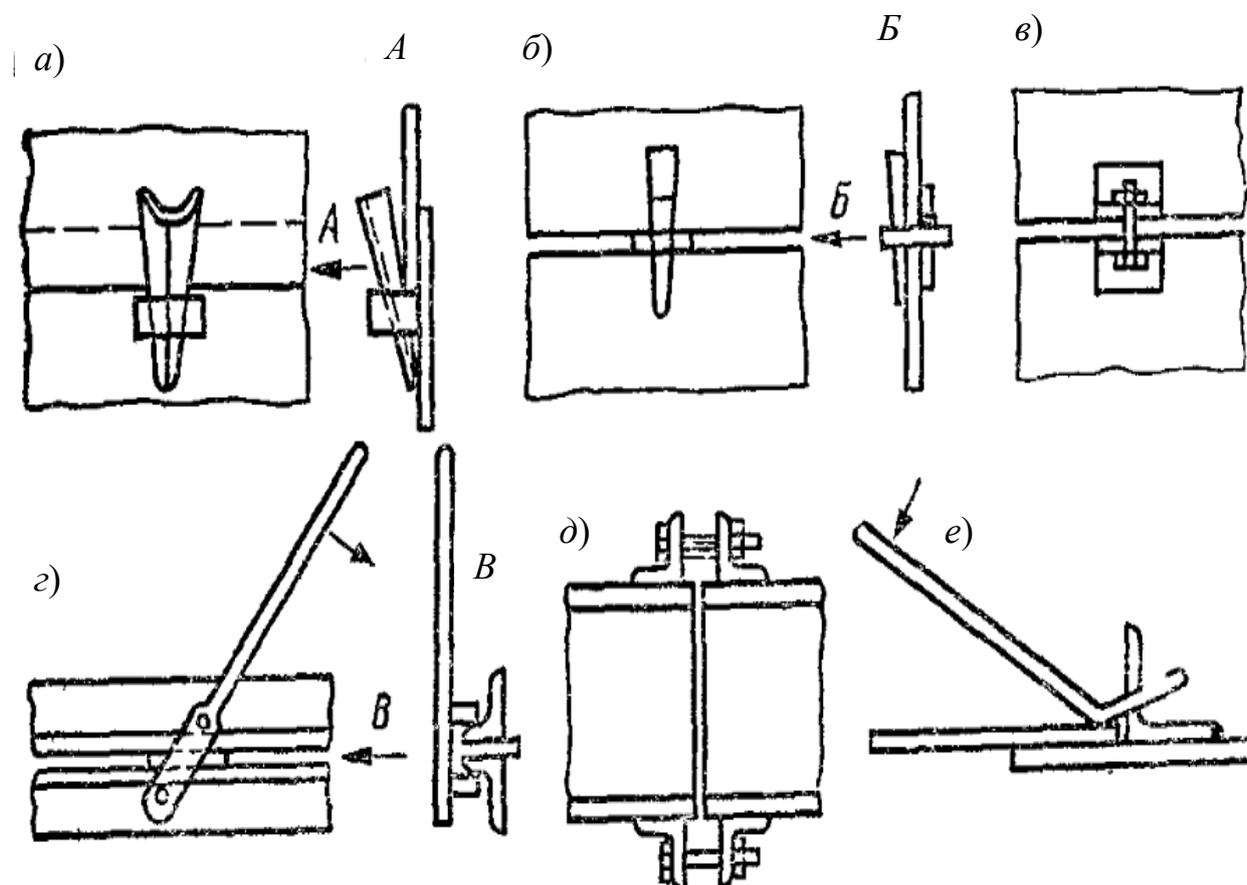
Сборка конструкций листовых (а–в), из профильного металла (г–е)
